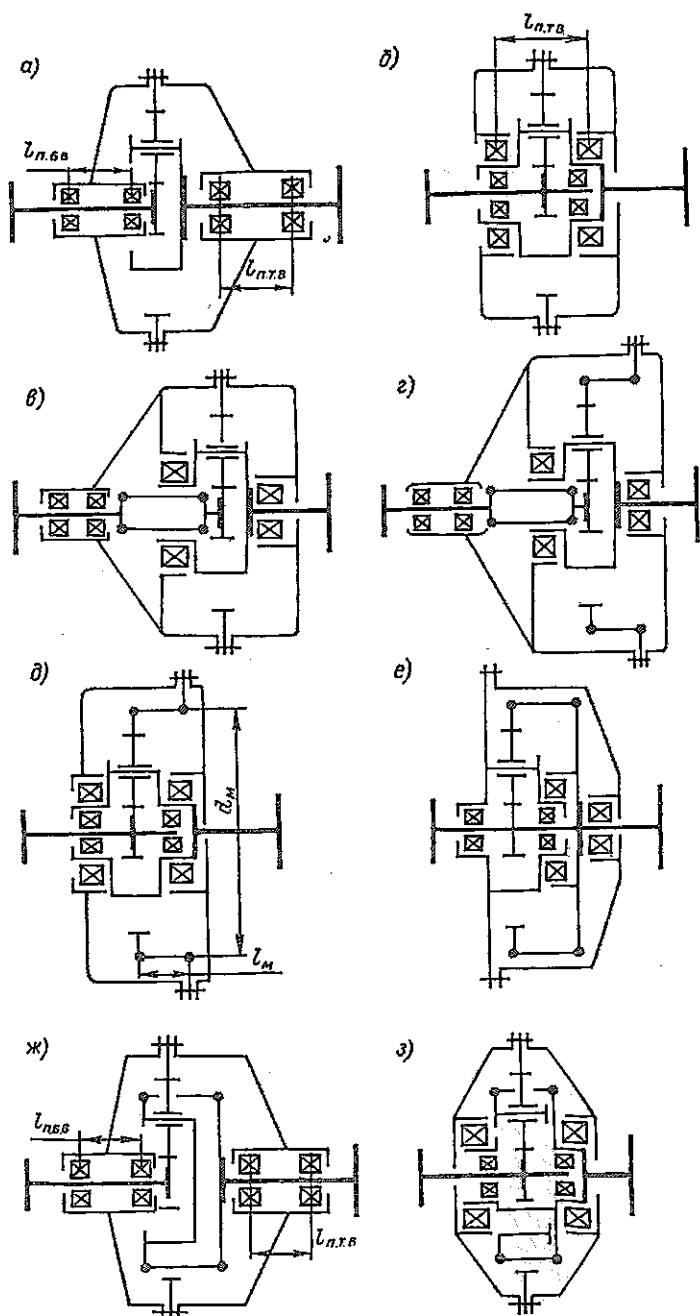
Компонентные схемы одноступенчатых редукторов с планетарными передачами $2k - h$, тип А
